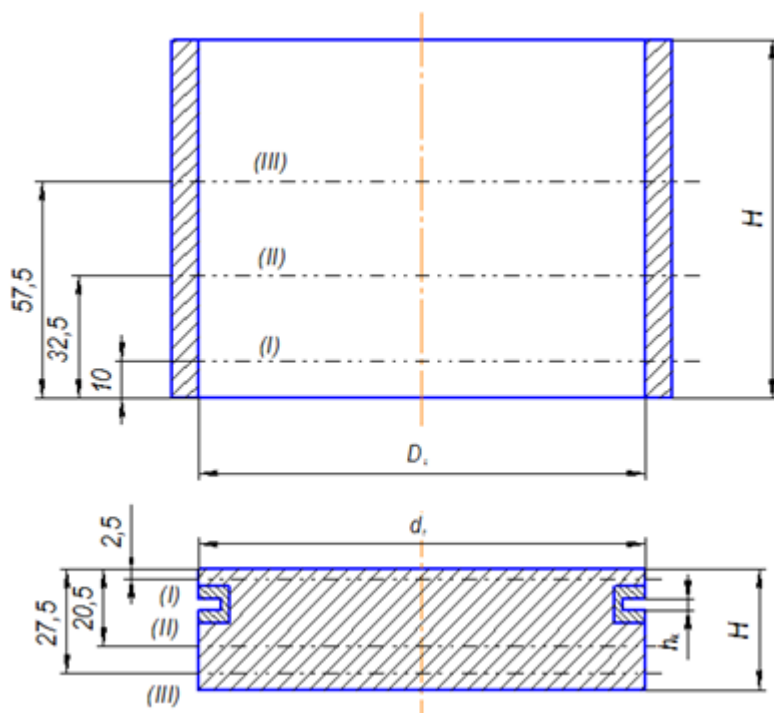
Схема микрометрирования размеров модельных деталей цилиндровой втулки (сверху) и поршня (снизу) двигателя 6Ч12/14СП (К-551)
